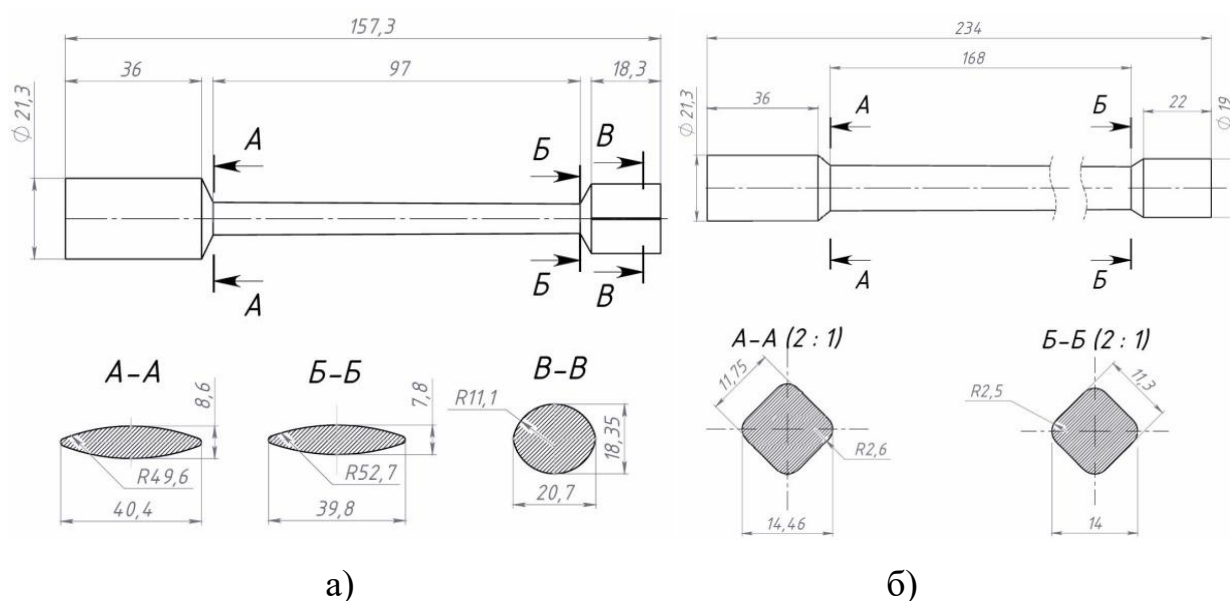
Форма и размеры заготовки после горячей вальцовки в ручьях переменного сечения: а – первый переход; б – второй переход
